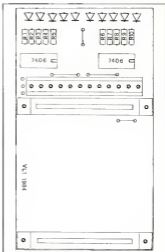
Assemblaggio dei componenti nel C5 VLJ
